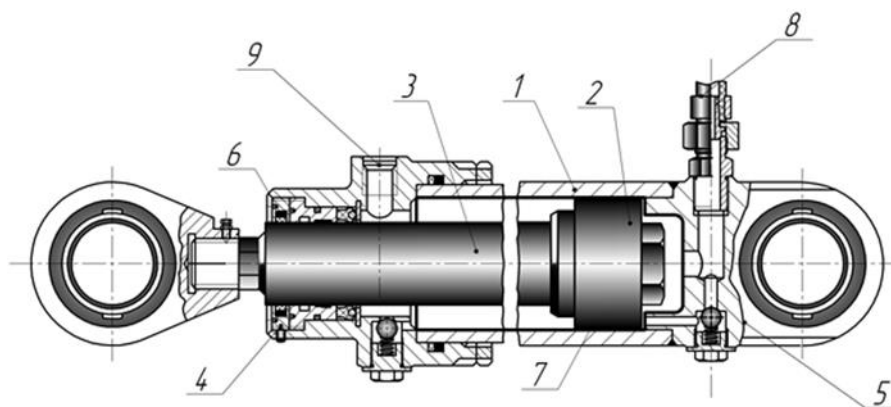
Схема конструкции гидроцилиндра двухстороннего действия с одним штоком
